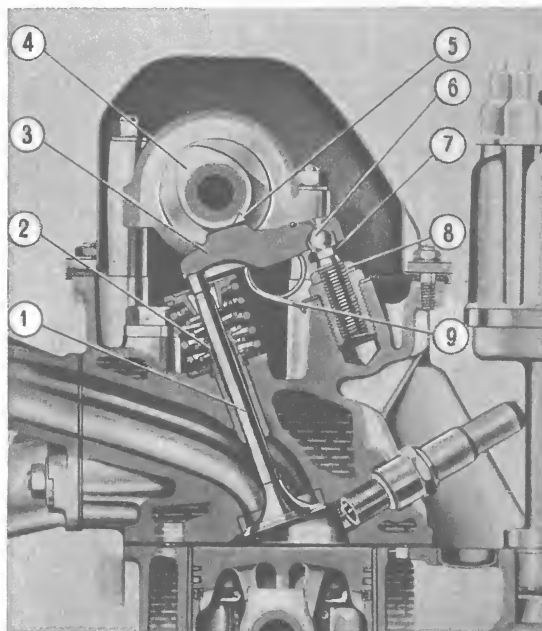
Клапанный механизм: 1 — клапан; 2 — защитный колпачок; 3 — рокер; 4 — распределительный вал; 5 — зазор между рокером и кулачком; 6 — сферическая головка регулировочного болта; 7 — шестигранник регулировочного болта; 8 — контргайка; 9 — шпильная пружина рокера.
